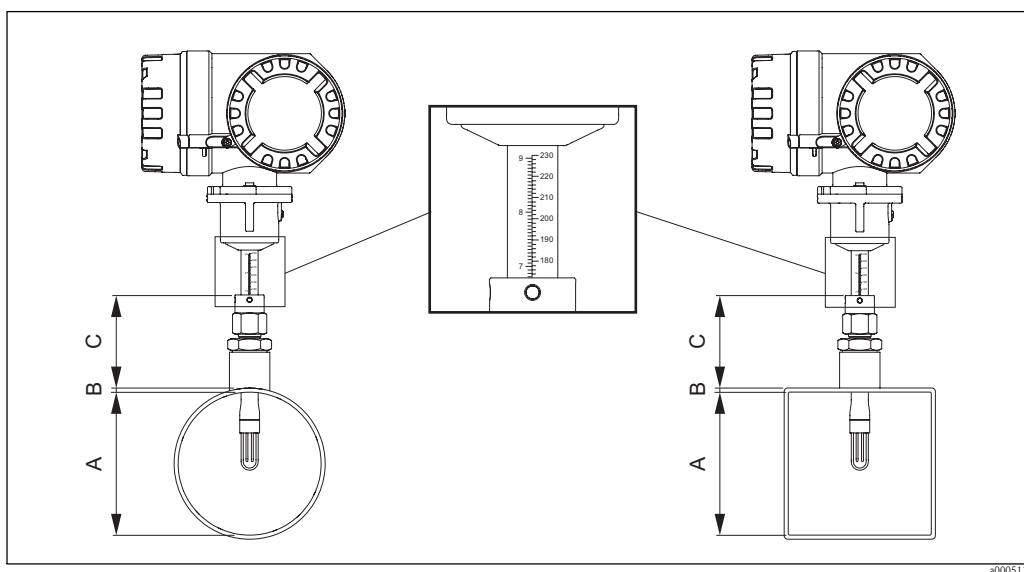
Dimensiones requeridas para calcular la profundidad de inserción del sensor
